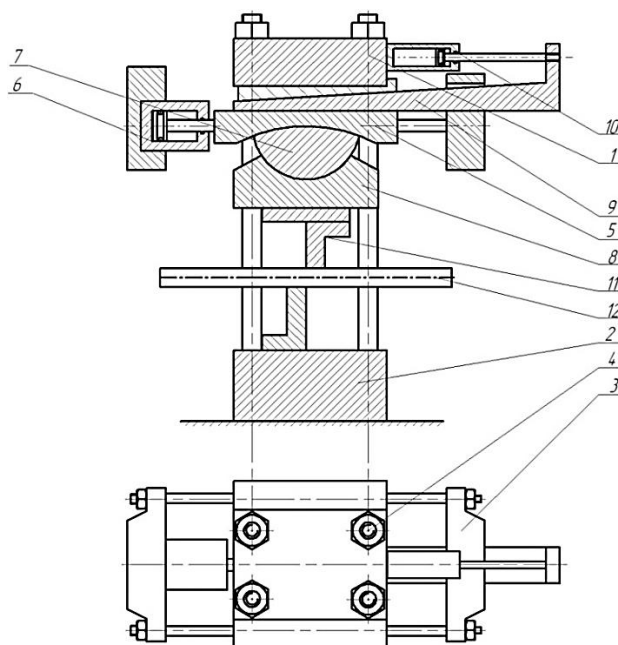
Конструктивная схема пресса с КШМ с ВК для разделения сортового проката отрезкой сдвигом
